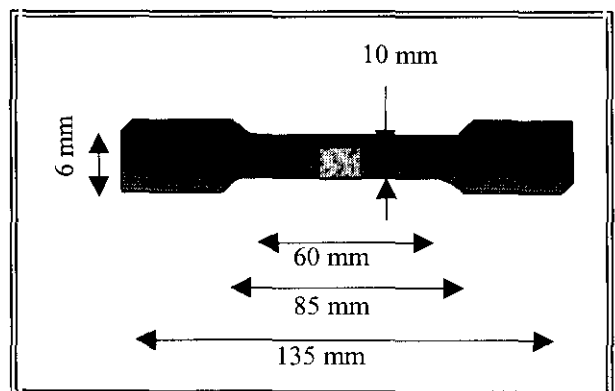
Probeta de tracción para uniones soldadas.
